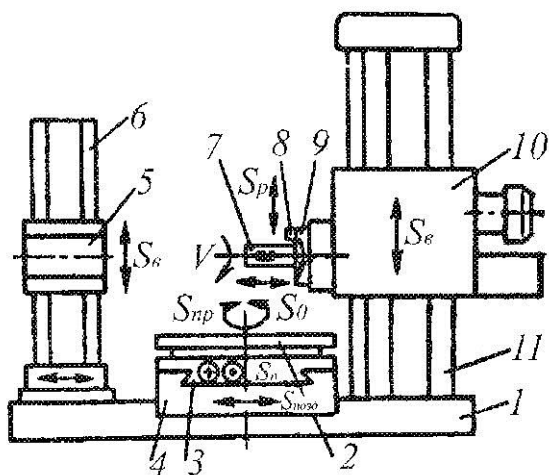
Загальний вид горизонтально-розточувального верстата
